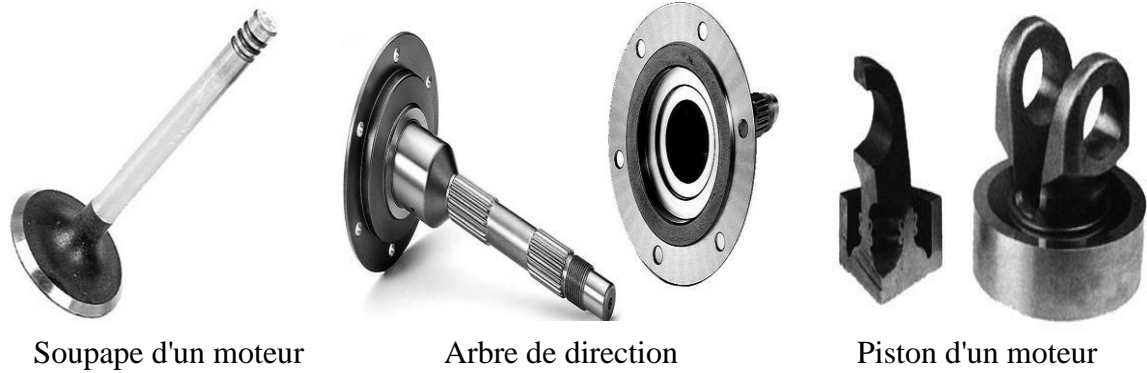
Quelques applications du soudage par friction rotative [3]
